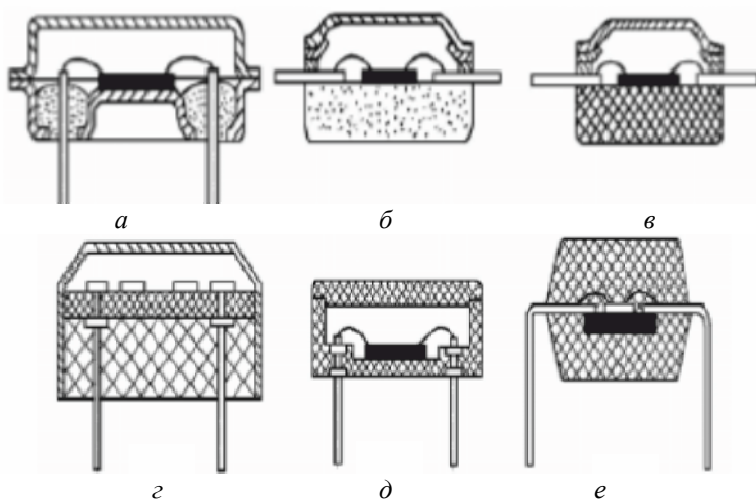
Конструкции корпусов: *a* – металлостеклянный; *б* – стеклянный; *в* – керамический; *г* – металлополимерный; *д* – пластмассовый; *е* – полимерный
